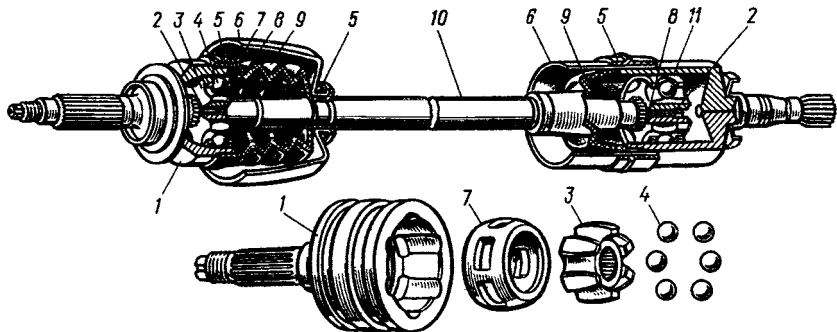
Привод передних колес автомобиля ВАЗ-2121:
